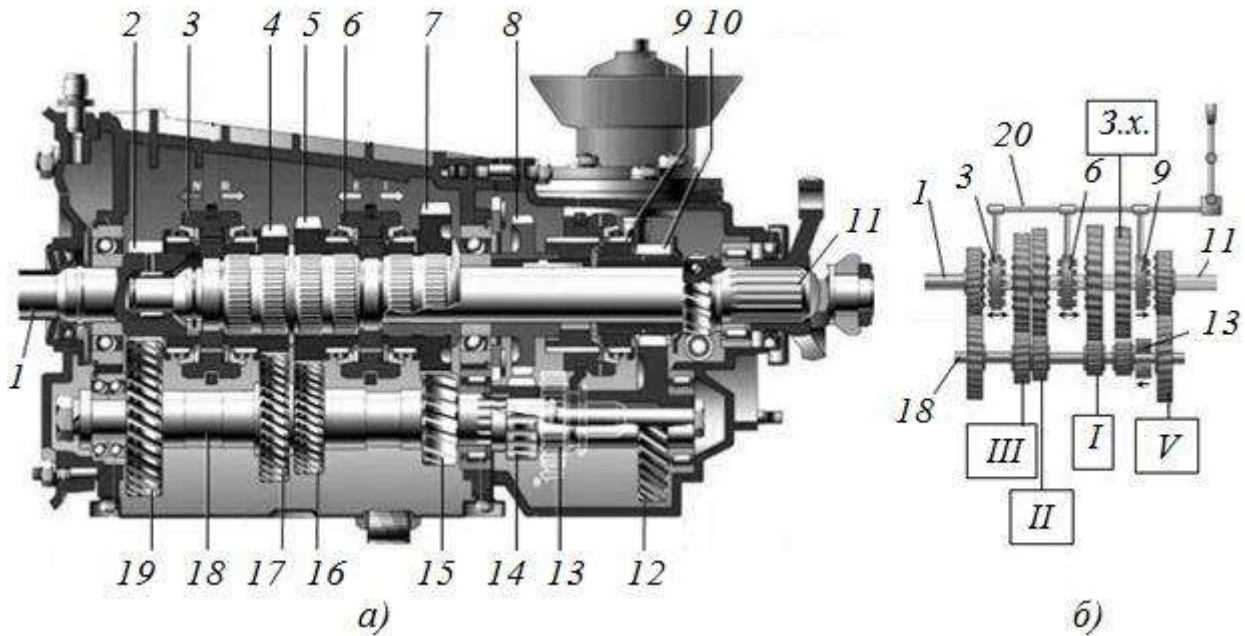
Розріз (а) та схема передач (б) трьохвальної коробки передач:
